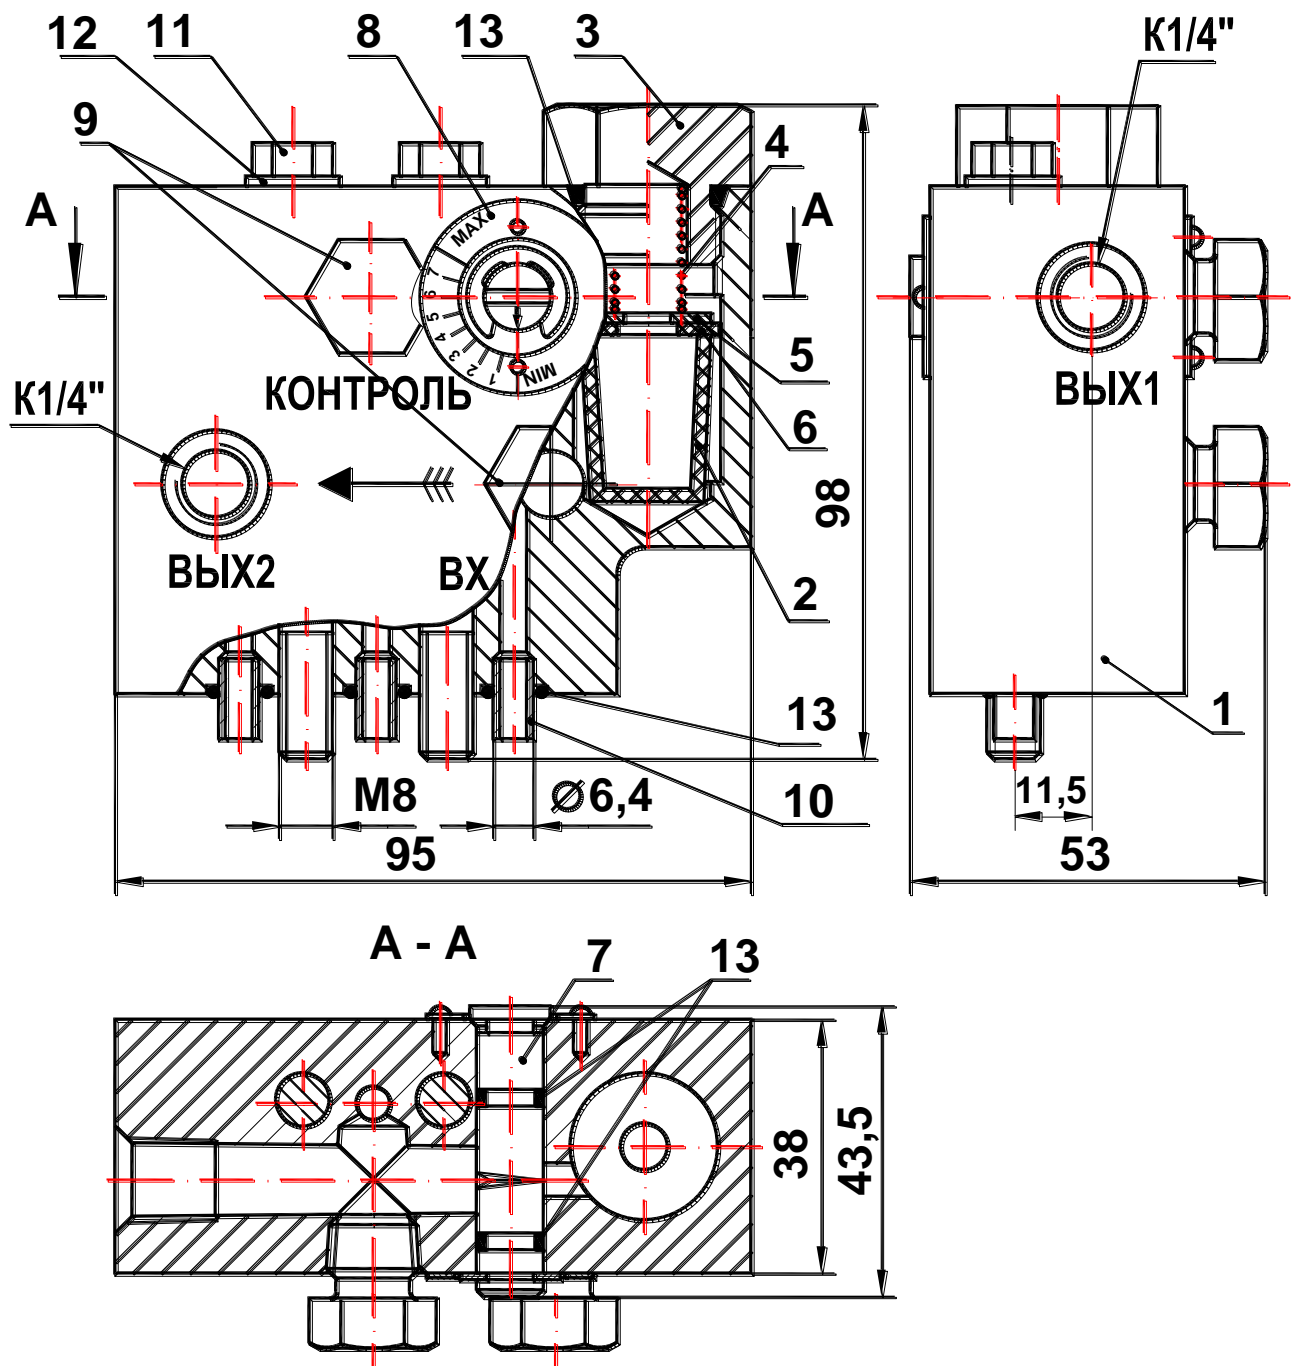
Устройство и габаритно-присоединительные размеры распределителя
